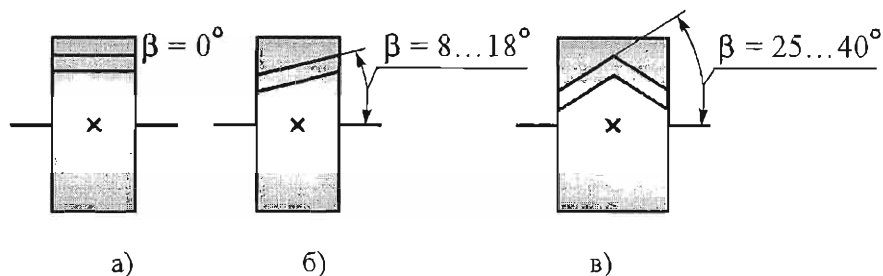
Направление зубьев цилиндрической зубчатой передачи относительно оси зубчатого колеса:
